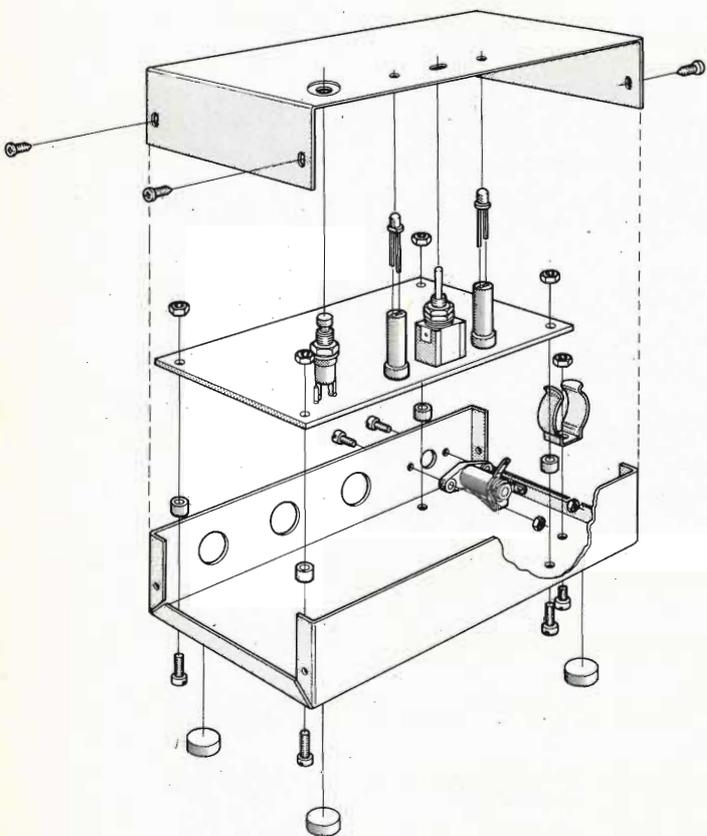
Assemblaggio del sincronizzatore per diapositive UK 873 dell'Amtron.
